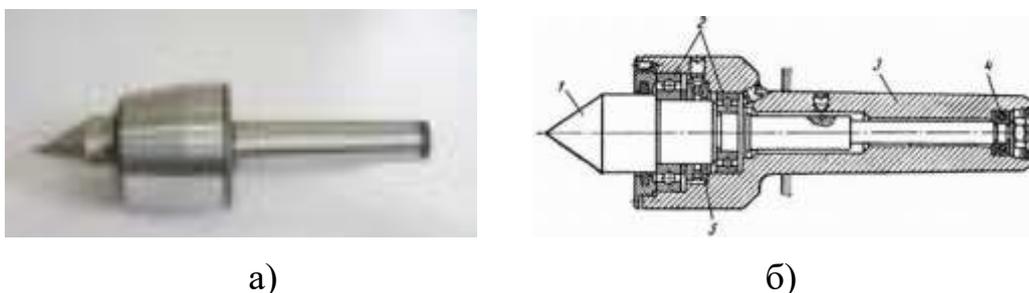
Центр задний а - общий вид, б - конструкция центра.
